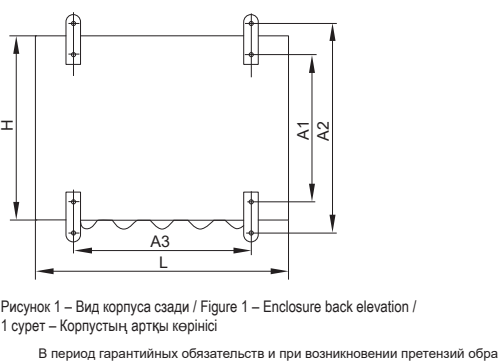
Вид корпуса сзади / Figure 1 – Enclosure back elevation / 1 сурет – Корпусың артқы көрінісі
